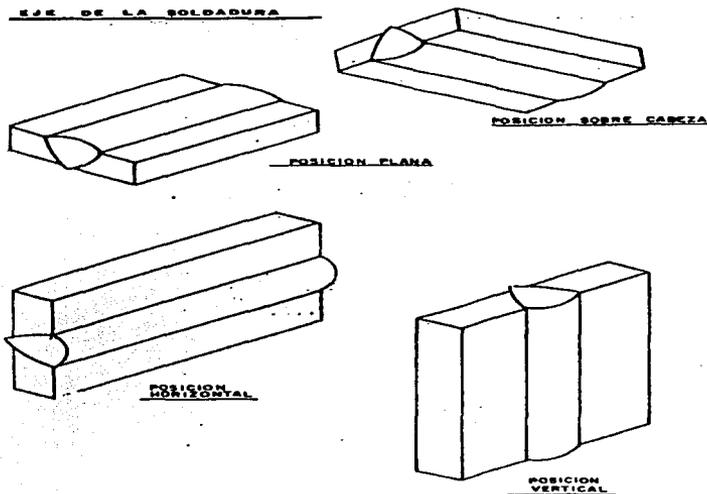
Posiciones que adopta un soldador al ir depositando los cordones a lo largo del bisel.
